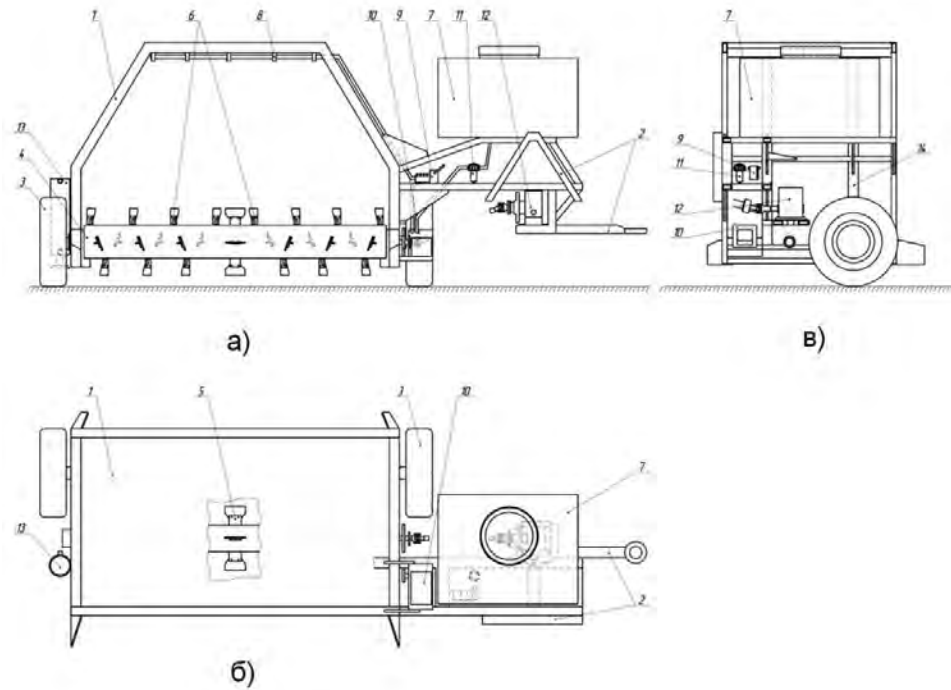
Конструктивна схема змішувача-аератора компосту: а – вид спереду, б – зверху; в – справа; 1 – рама; 2 – зчіпка; 3 – опорні колеса; 4 – фрезерний обертовий барабан з робочими елементами; 5, 6 – плоскі лопати; 7 – місткість для рідких компонентів; 8 – розпилювачі; 9 – розподільник; 10 – насос; 11 – фільтр; 12 – редуктор; 13 – гідродомкрат; 14 – гвинтові вали
